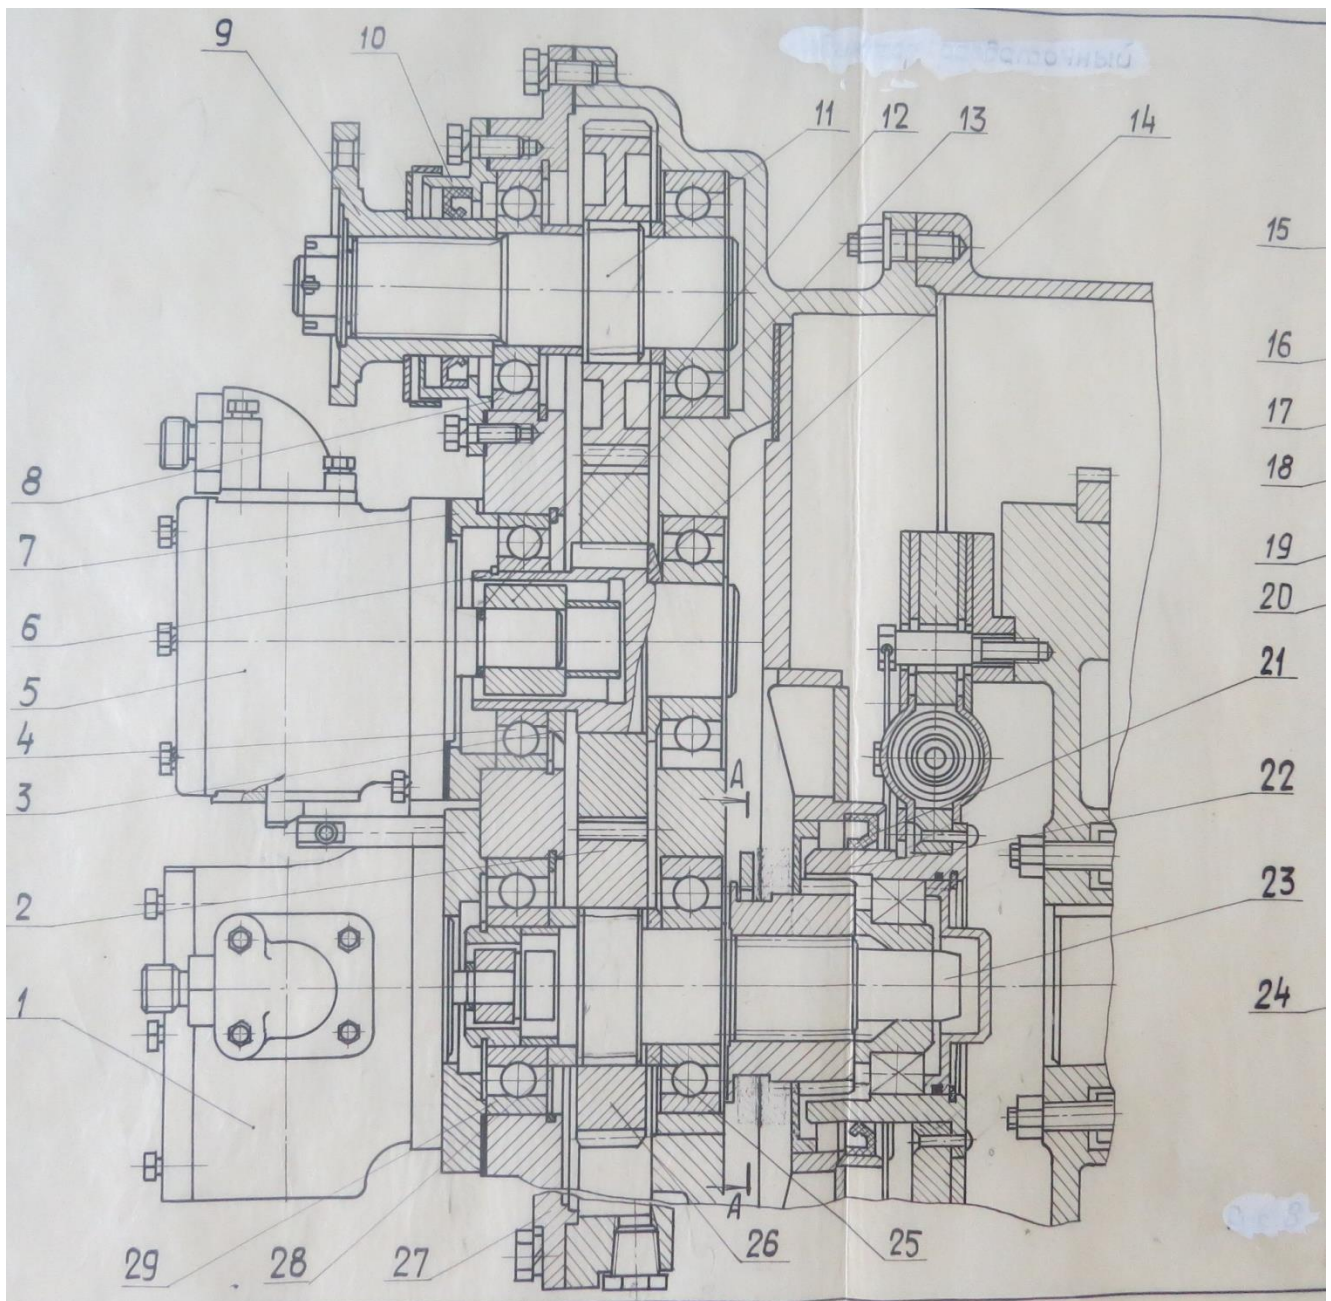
Схема роздавального редуктора шасі 1BOM.01A:
